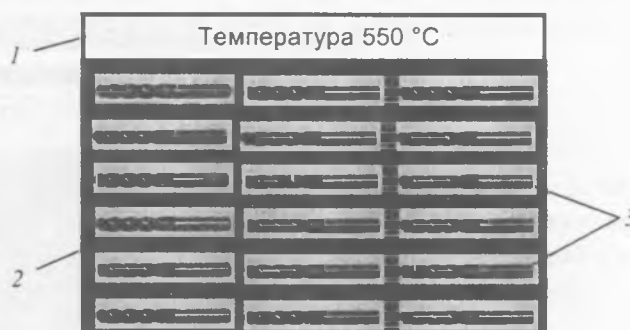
Схема процесса диффузионного насыщения фрез: 1 — контейнер, закрытый крышкой с песчаным затвором; 2 — диффузионно-активная порошковая смесь; 3 — обрабатываемые фрезы
